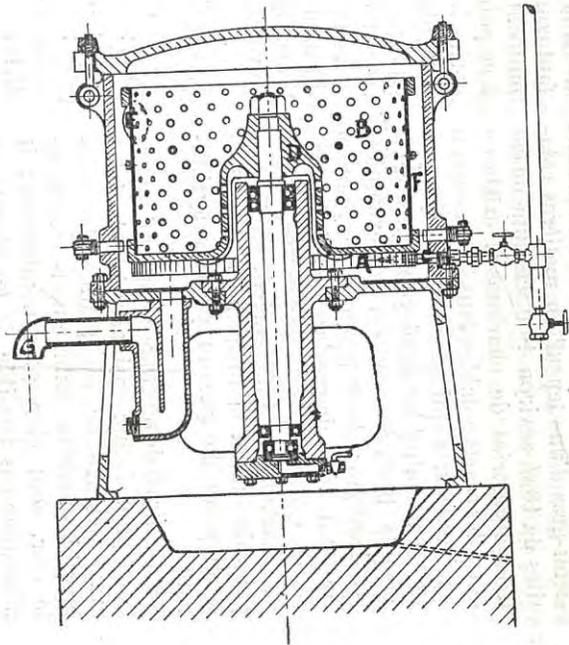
Extracteur-séparateur centrifuge à turbine.
